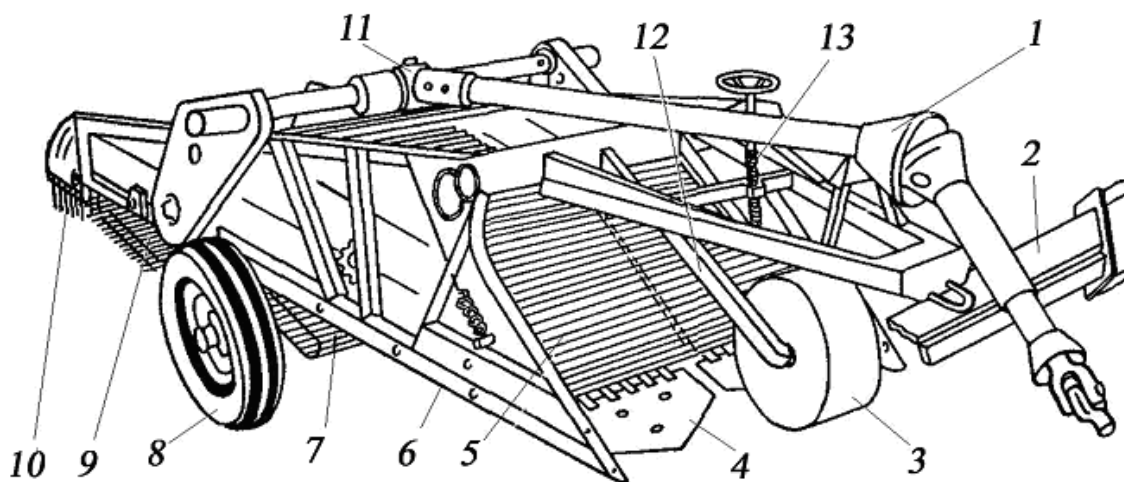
Картоплекопач швидкісний КСТ-1,4: 1 - карданна передача; 2 - поперечина начіпного пристрою; 3 - копіювальне колесо; 4 - леміш. 5 - швидкісний елеватор; 6 - рама; 7 - основний елеватор; 8 - ходове колесо; 9 - каскадний елеватор; 10 - відбивач; 11 - редуктор; 12 - рамка копіювального колеса; 13 - гвинтовий механізм
